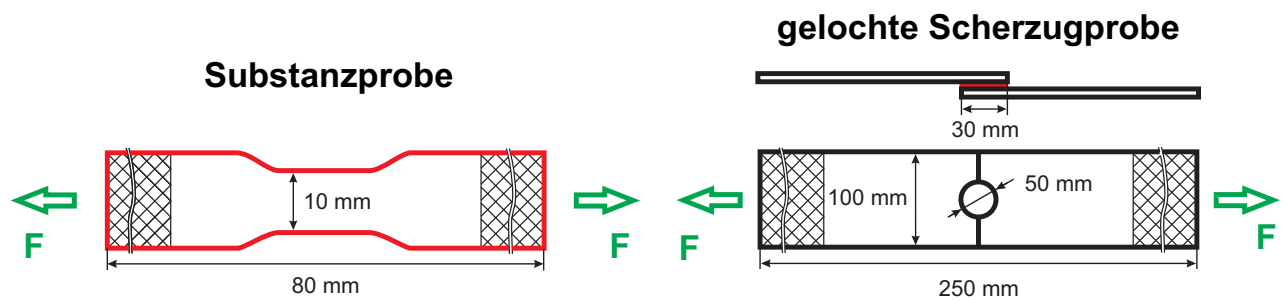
Verallgemeinerte Geometrie geschweißter und HVB-gefügter Proben
